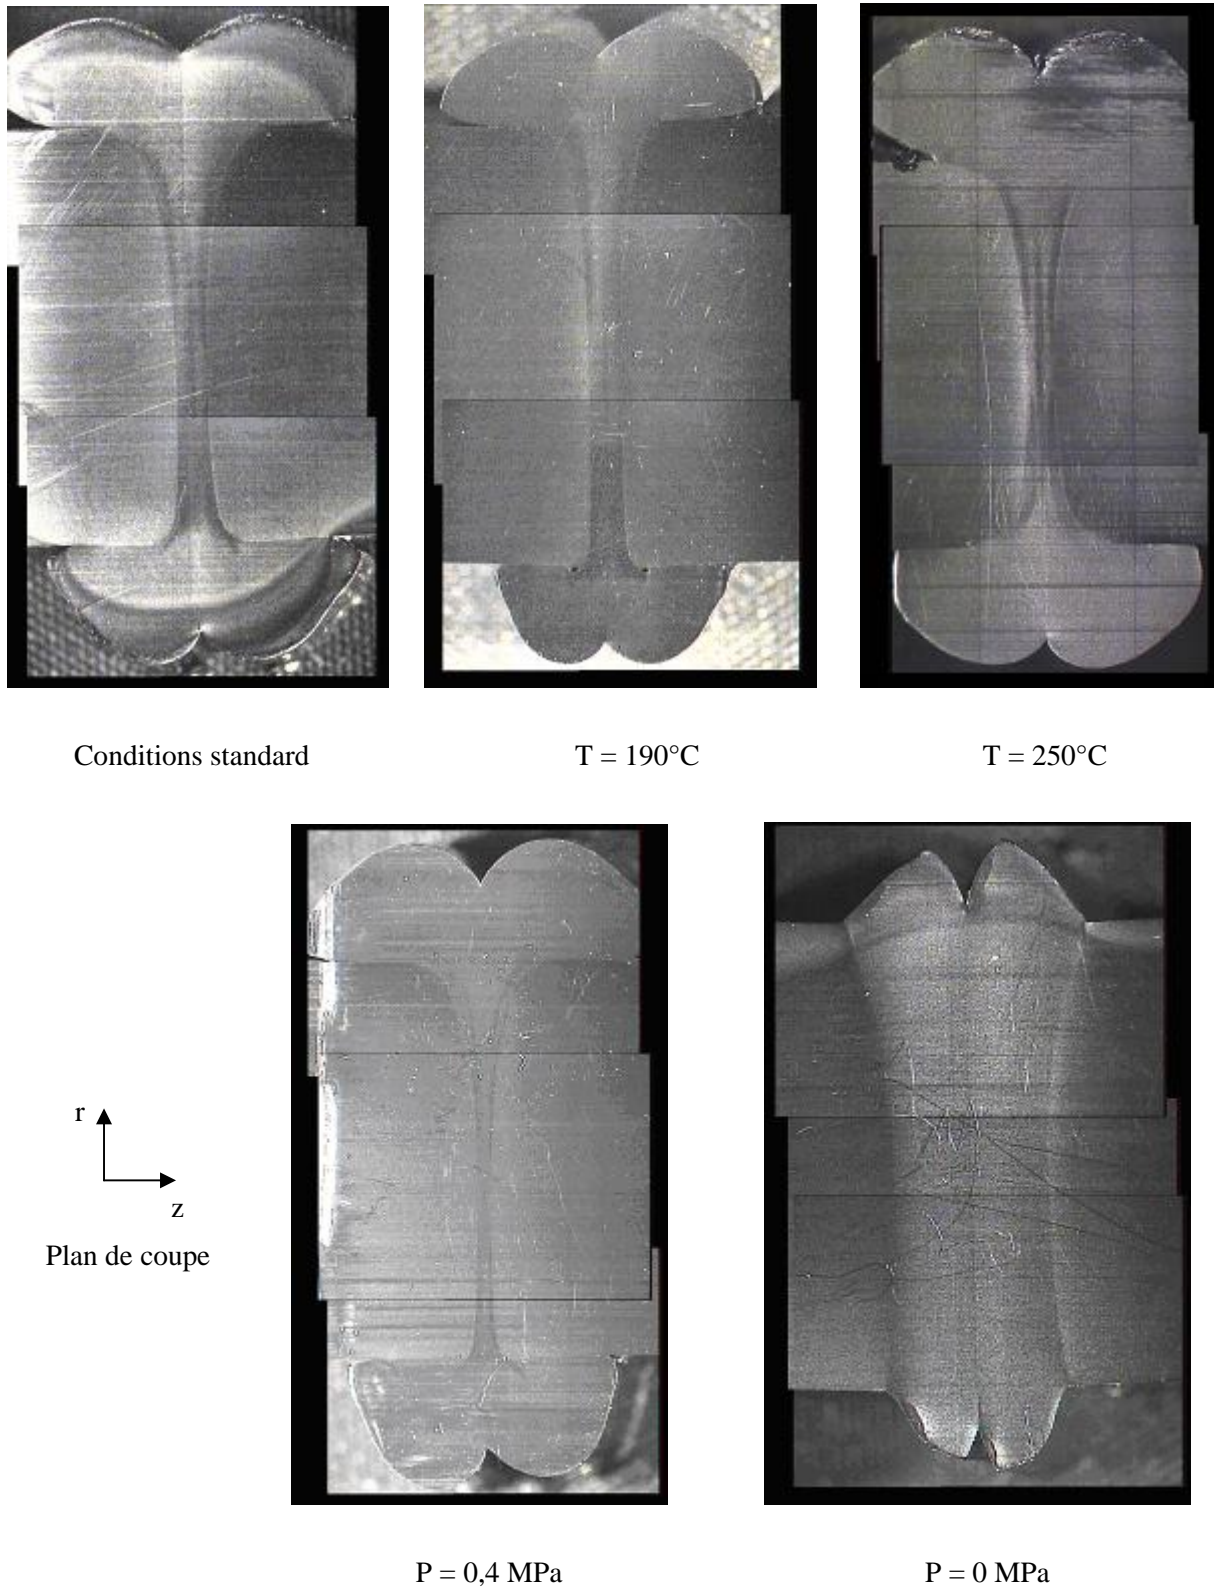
Clichés des soudures obtenues après l'essai du "sèche-cheveux" pour différentes conditions de soudage
